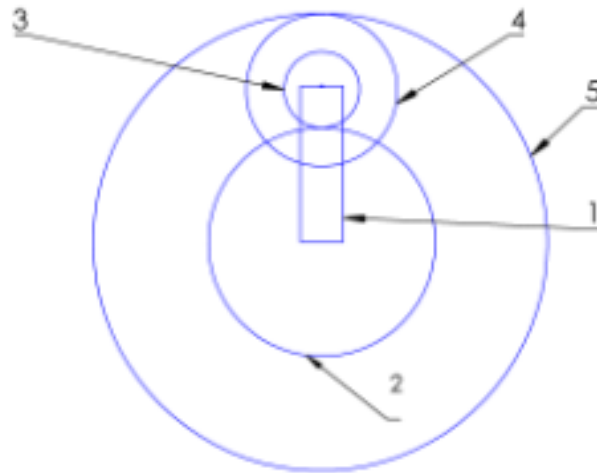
Vista principal do trem de engrenagens [Autor]
